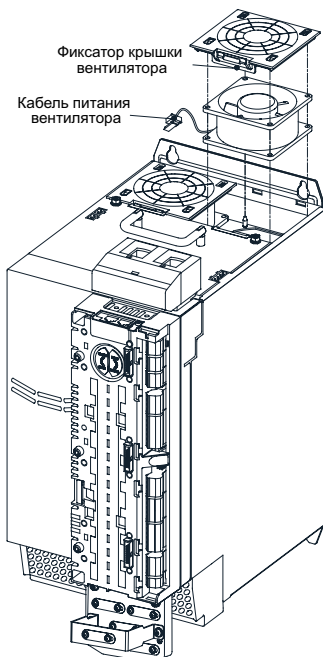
Замена вентилятора инверторного блока типоразмера Н4
